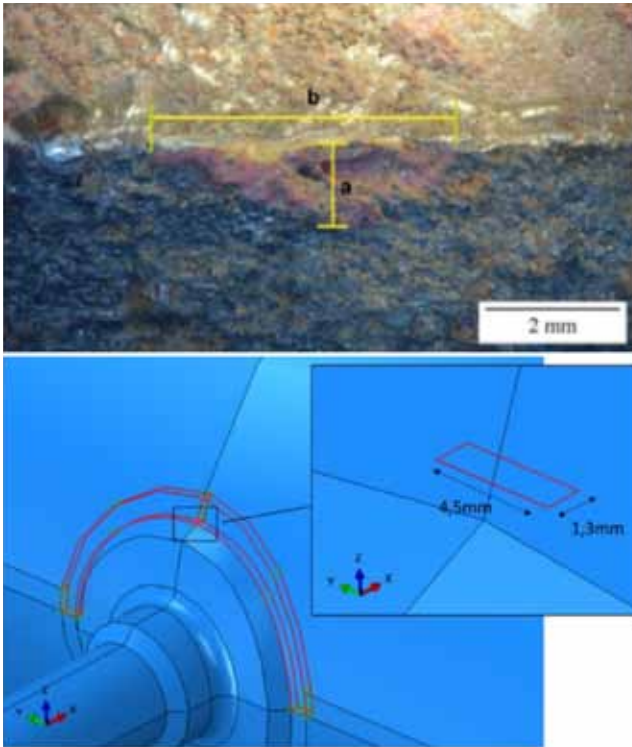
Dimensiones del defecto inicial: a = 1.3 mm, b = 4.5 mm
